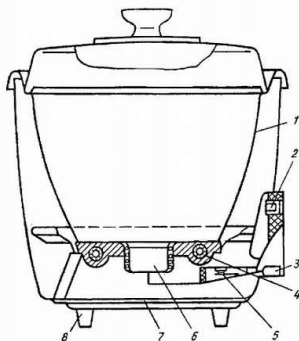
Конструкция электрорисоварки: 1 — внутренний сосуд; 2 — клавишное устройство; 3 — сигнальная лампа; 4 — электронагреватель; 5 — контактное устройство; 6 — стакан; 7 — наружный сосуд; 8 — подставка
